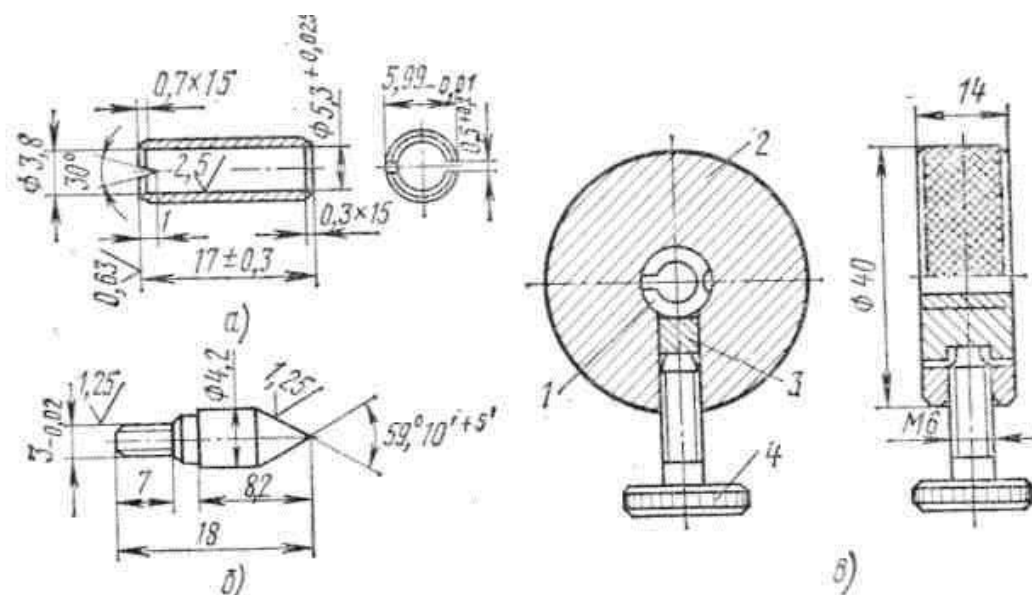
Притирочные приспособления для ремонта деталей распылителя форсунки:
